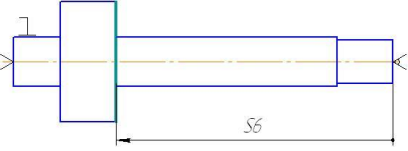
Ескіз заготовки з контурами деталі і технологічною розміткою основних поверхонь
